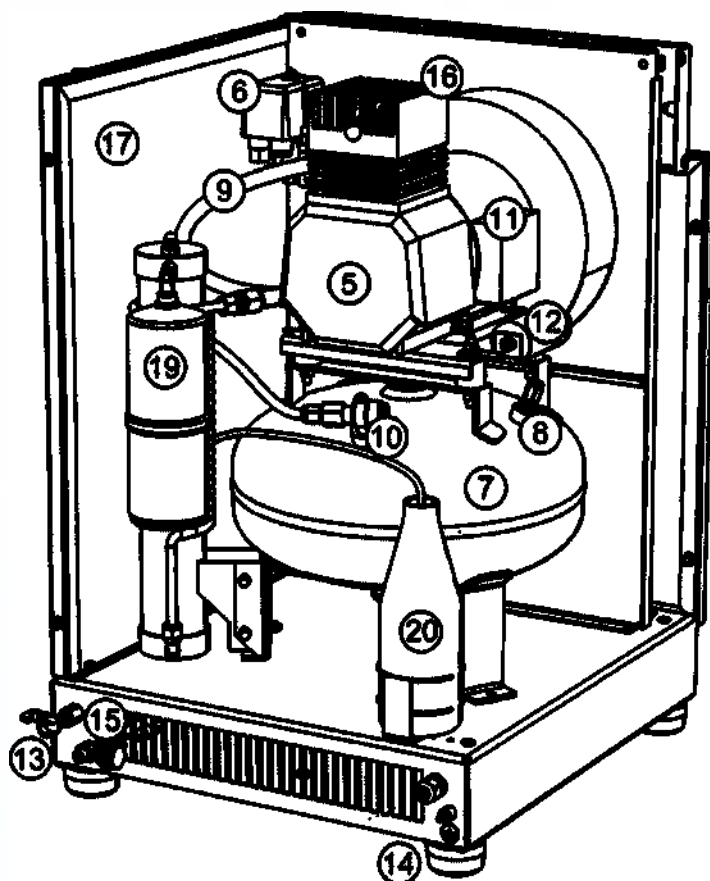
Общий вид компрессора KM-16.GMS150KD
